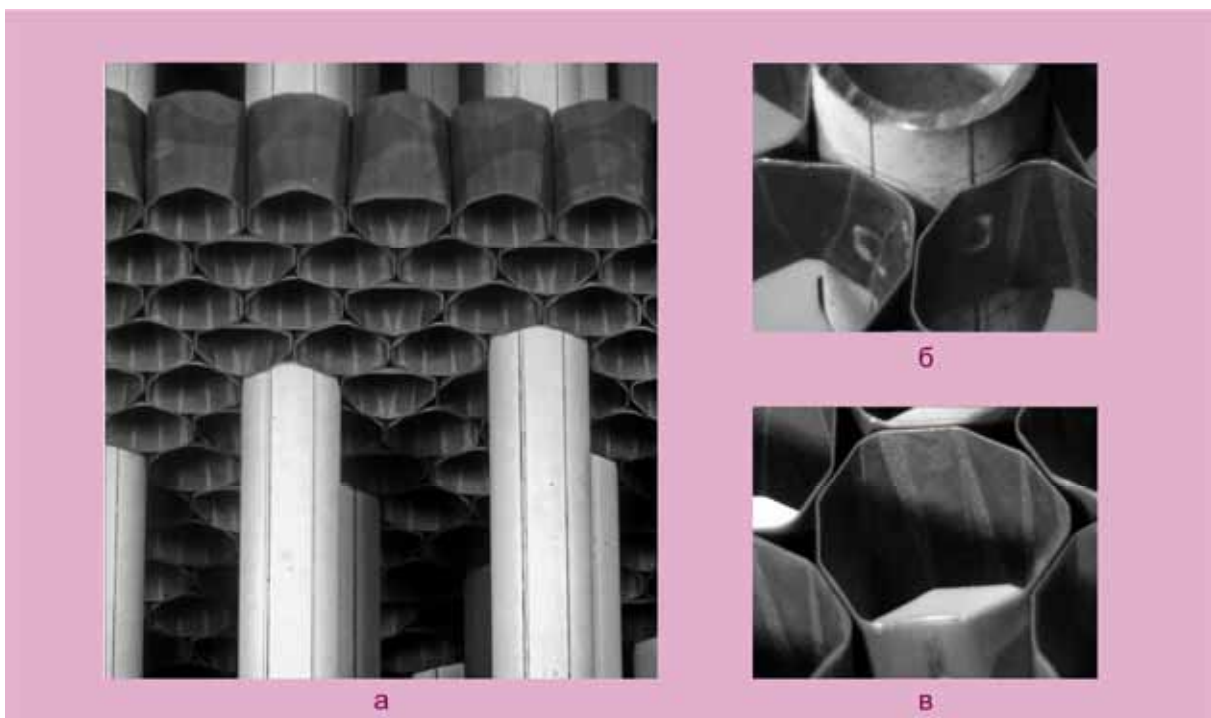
Внешний вид перемешивающей решётки в пучке (а) и сварных соединений «ячейка–направляющий канал» (б) и «ячейка–ячейка» (в)
